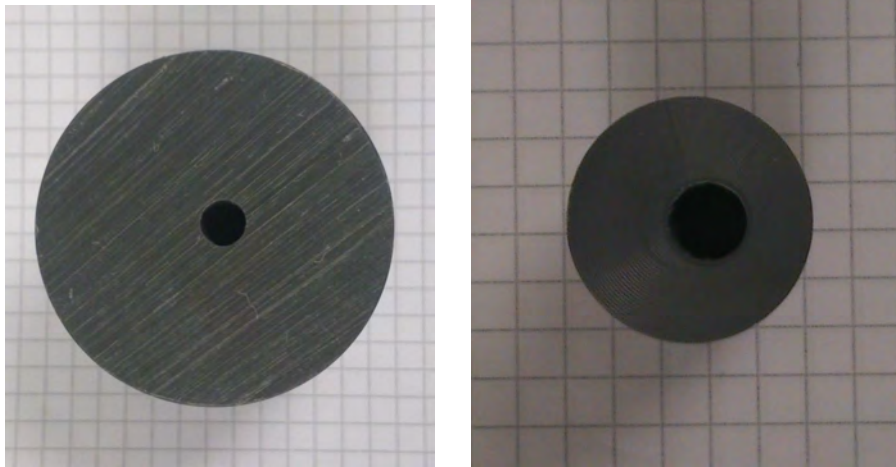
Exzentrischer Hohlzylinder zur Ausmessung der y-Achse links und der xz-Achse rechts, des ersten Auslese-Boards
